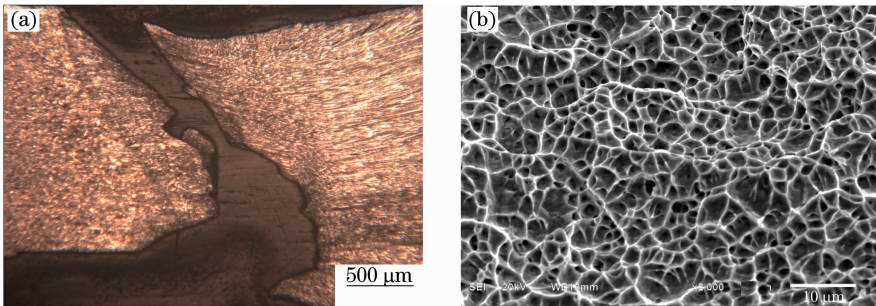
焊缝拉伸断裂位置及断口形貌
